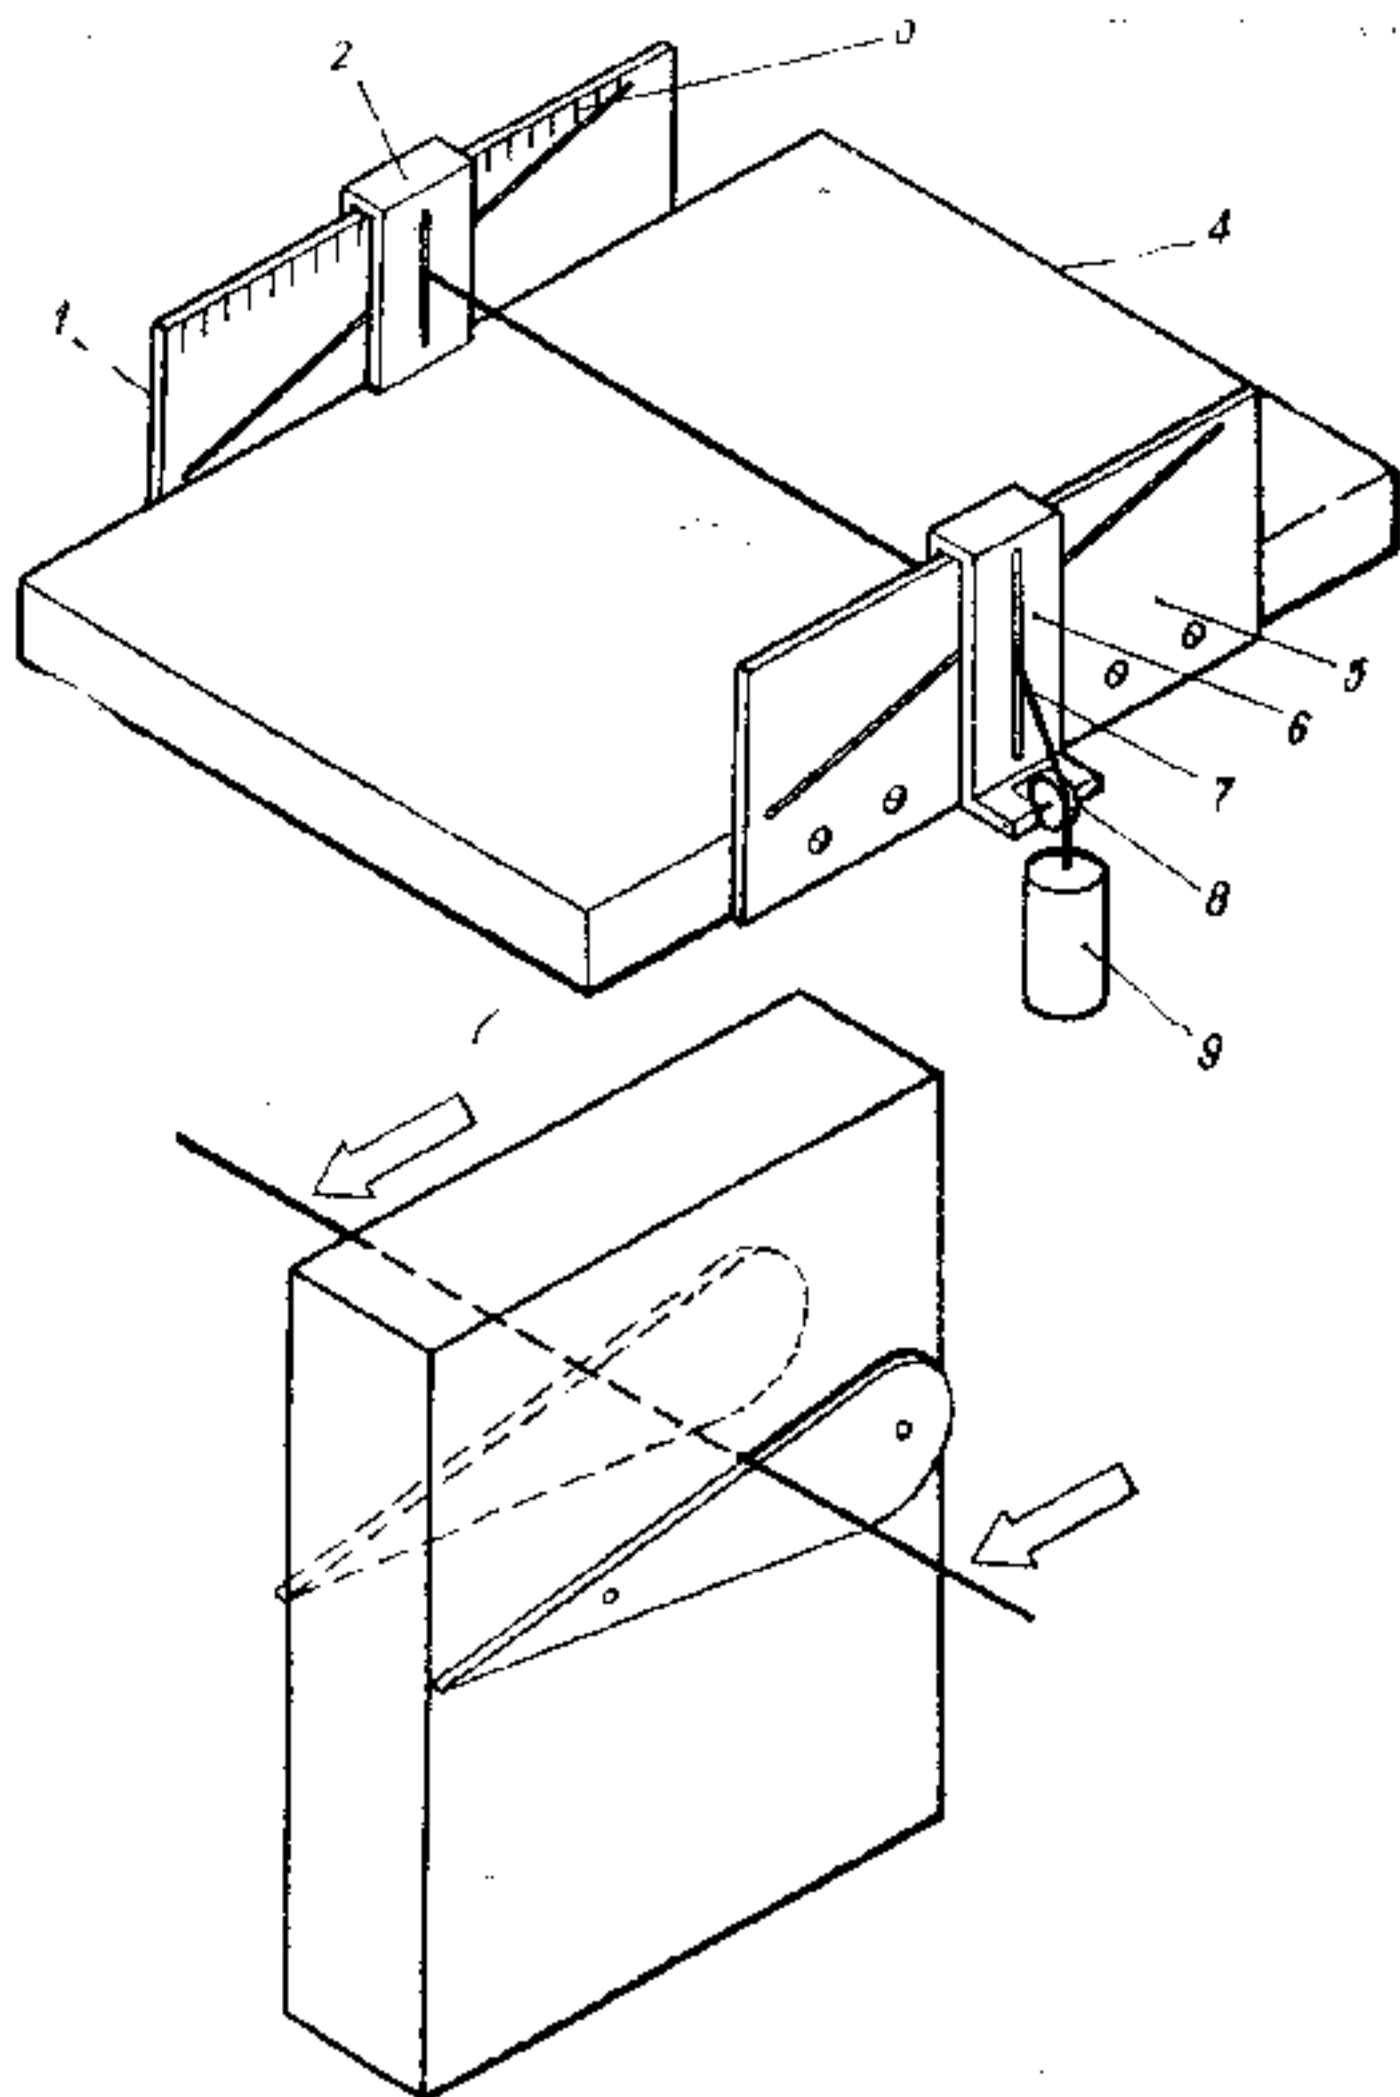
Приспособление для изготовления пластин заполнителя.
